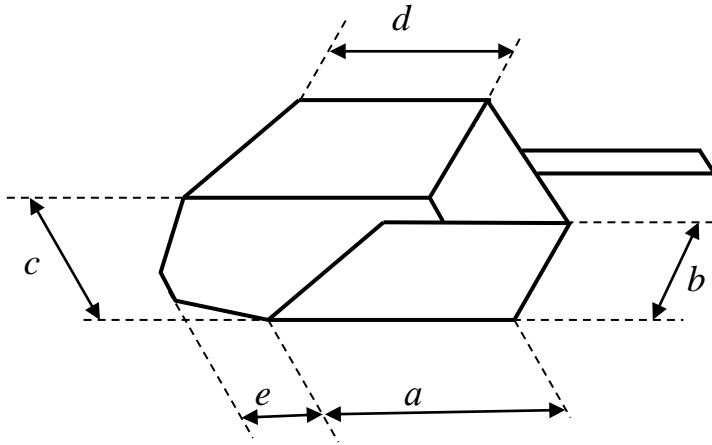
Загальний вигляд стандартного совка та його розміри
